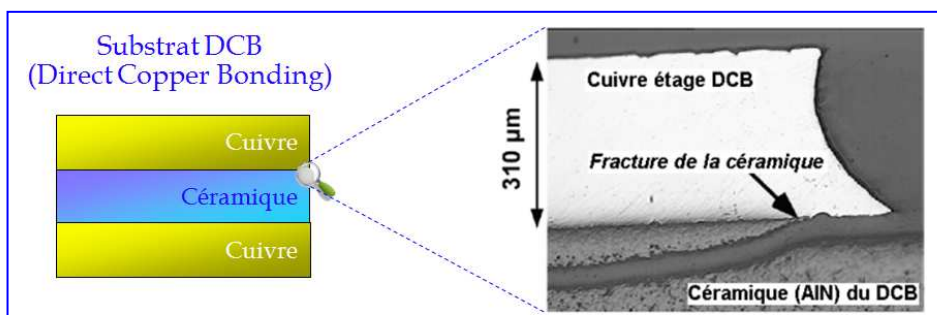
fracture de la céramique du DCB après cyclages thermiques passifs -30 °C / +180 °C [42].
